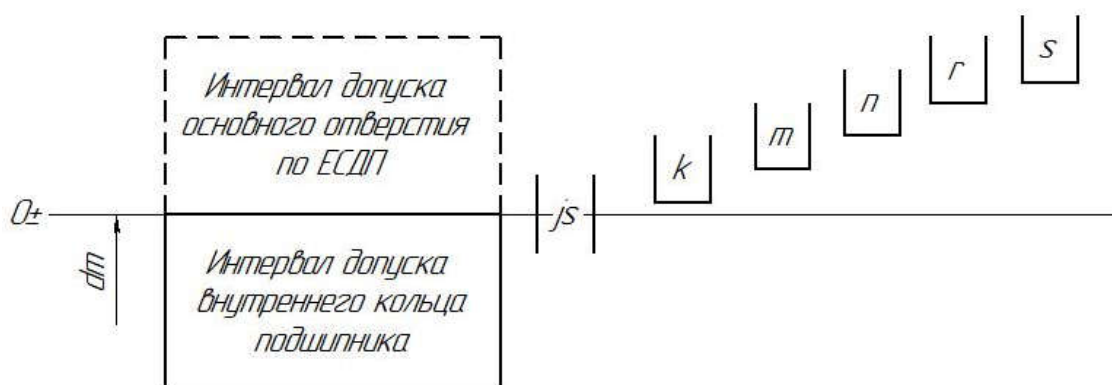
Схема расположения некоторых основных отклонений валов и посадочного интервала допуска внутреннего кольца подшипника
